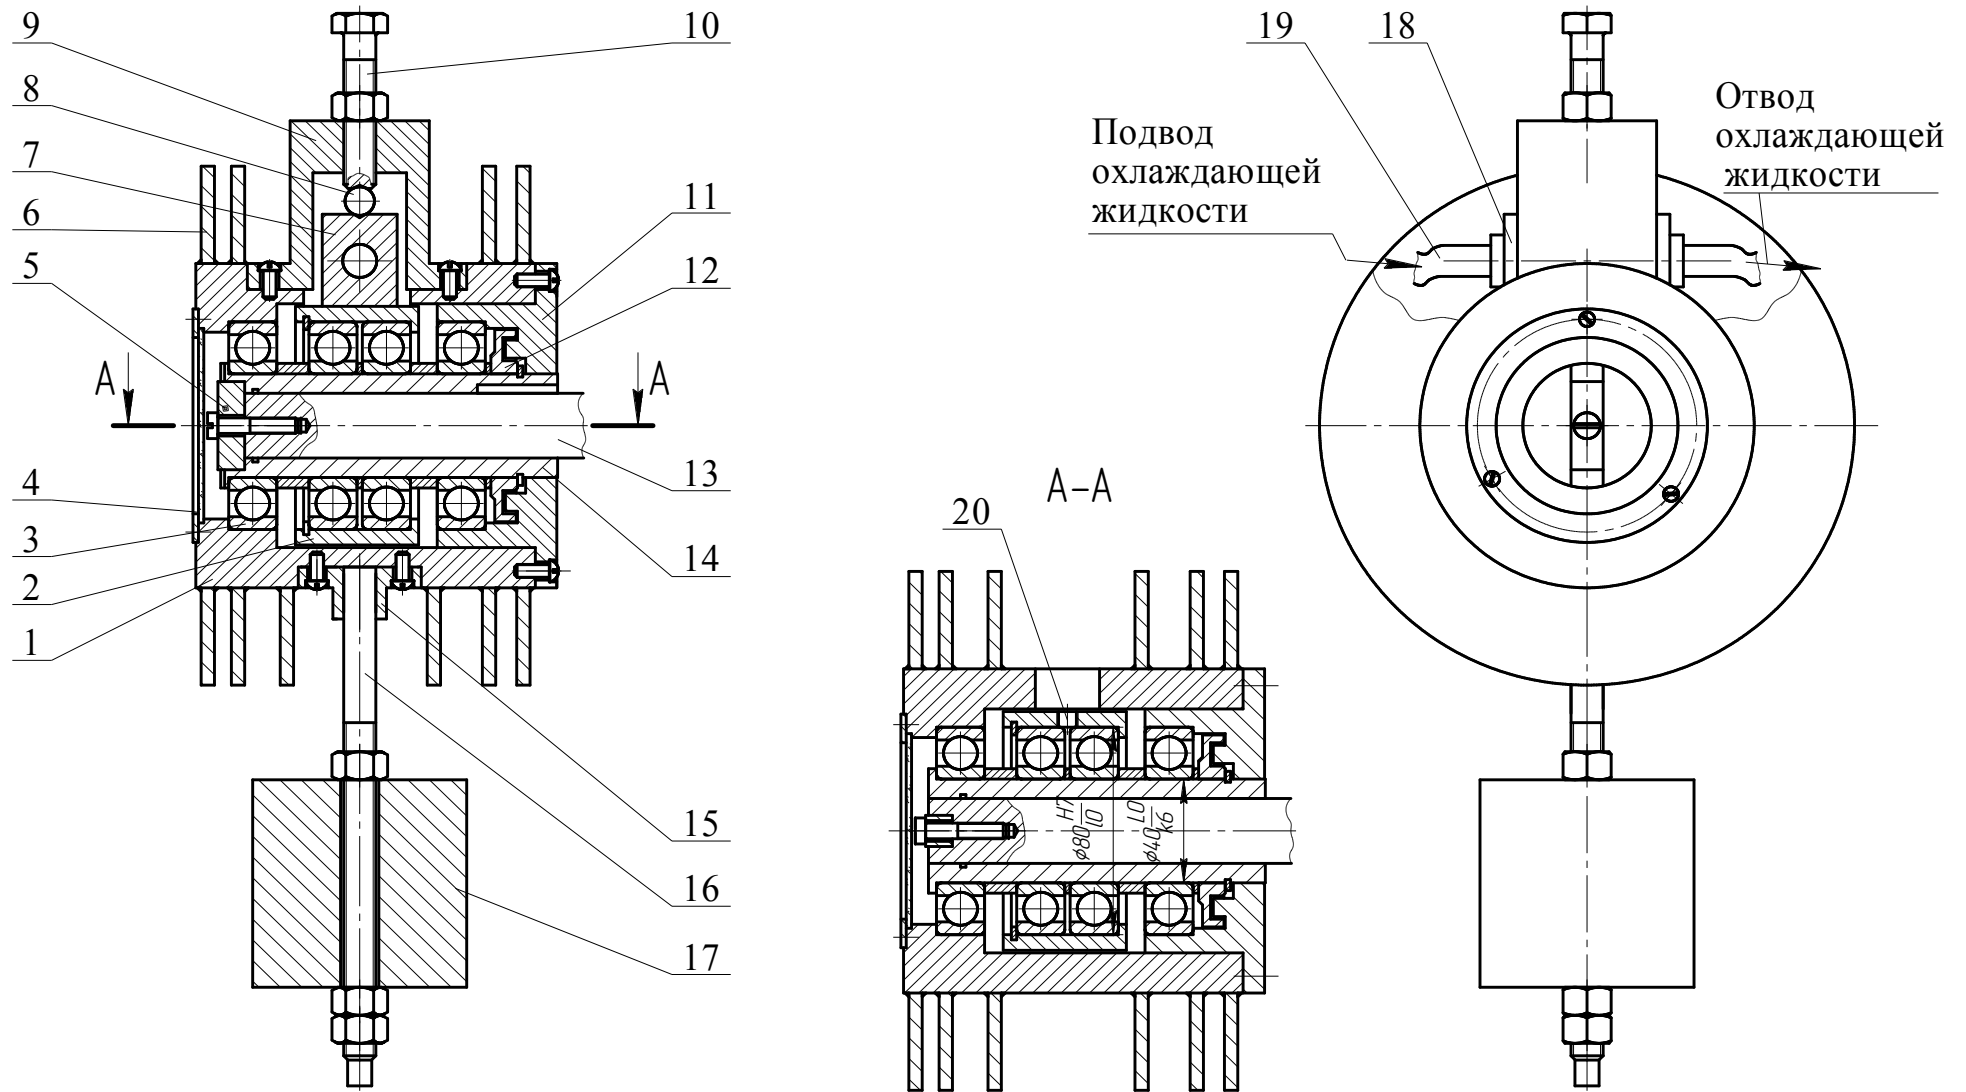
Подшипниковый узел в сборе: 1 – корпус, 2 – обойма, 3 – подшипник, 4 – крышка, 5 – шпонка, 6 – диск радиатора охлаждения, 7 – башмак, 8 – шарик, 9 – кронштейн, 10 – винт, 11 – крышка, 12 – кольцо, 13 – приводной вал, 14 – полый вал, 15 – фланец, 16 – стержень, 17 – груз, 18 – штуцер, 19 – шланг, 20 – канал для подачи смазки
